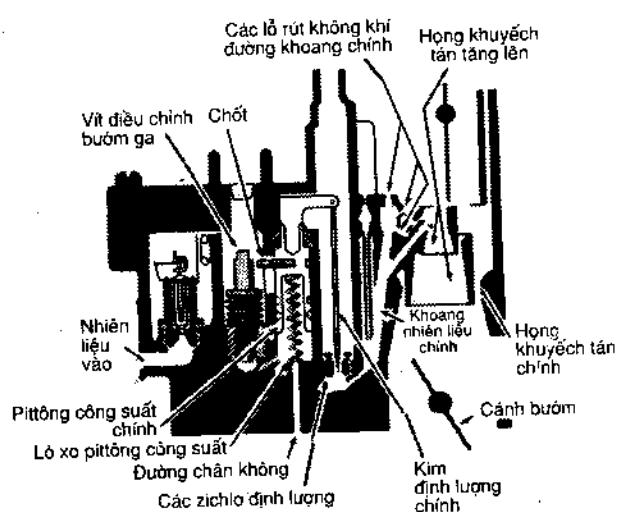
Hệ thống toàn tải điều khiển cơ khí.
